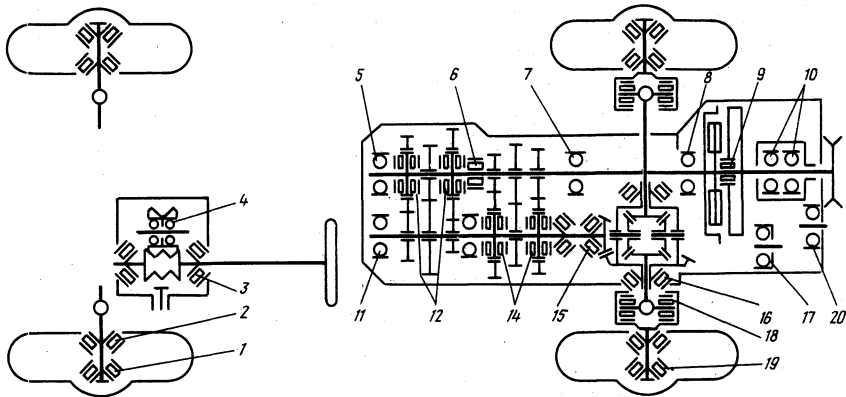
Схема расположения подшипника качения на «Запорожце» ЗАЗ-968:
